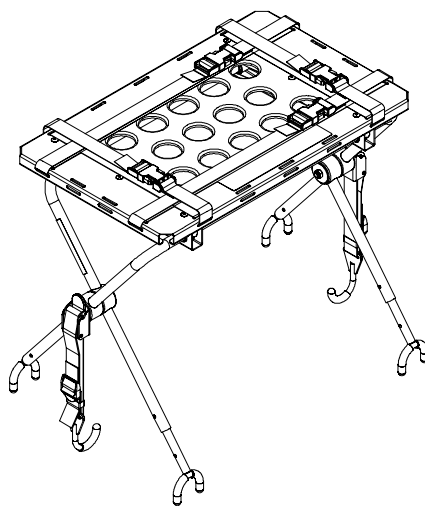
Ouvrir les pieds du plateau porte-défibrillateur
